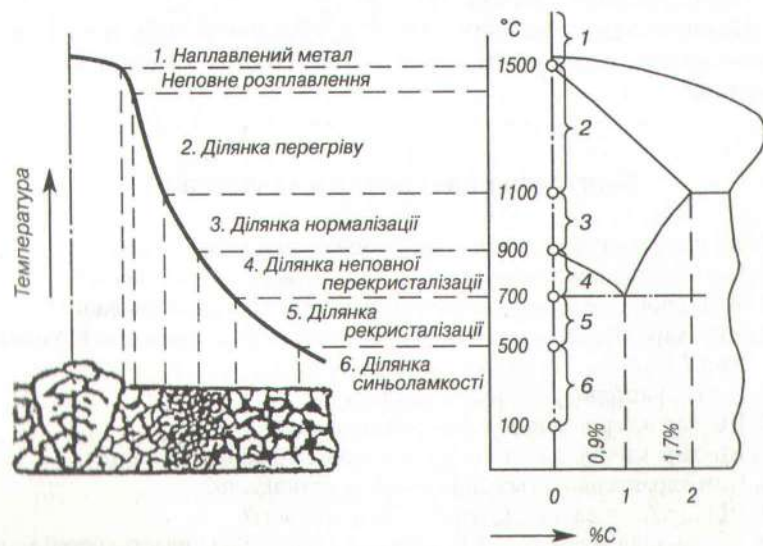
Будова зони термічного впливу зварного з'єднання
